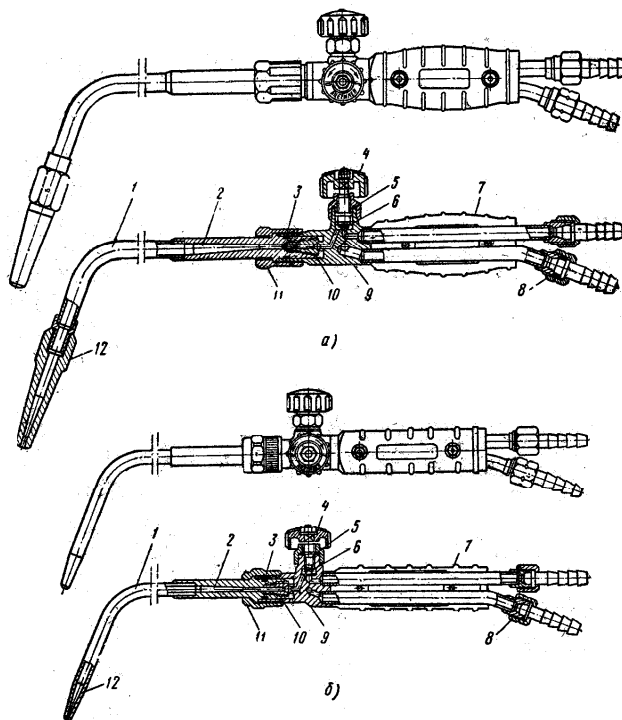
Внешний вид и разрез инжекторных горелок:
